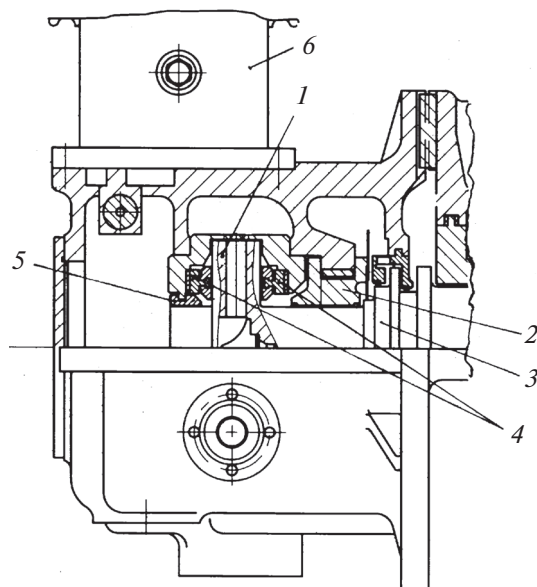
Типовой передний подшипник турбин малой мощности ОАО КТЗ. 1 – насос-регулятор; 2 – опорный подшипник; 3 – вал ротора турбины; 4 – упорный подшипник; 5 – плавающее уплотнительное кольцо; 6 – блок регулирования
